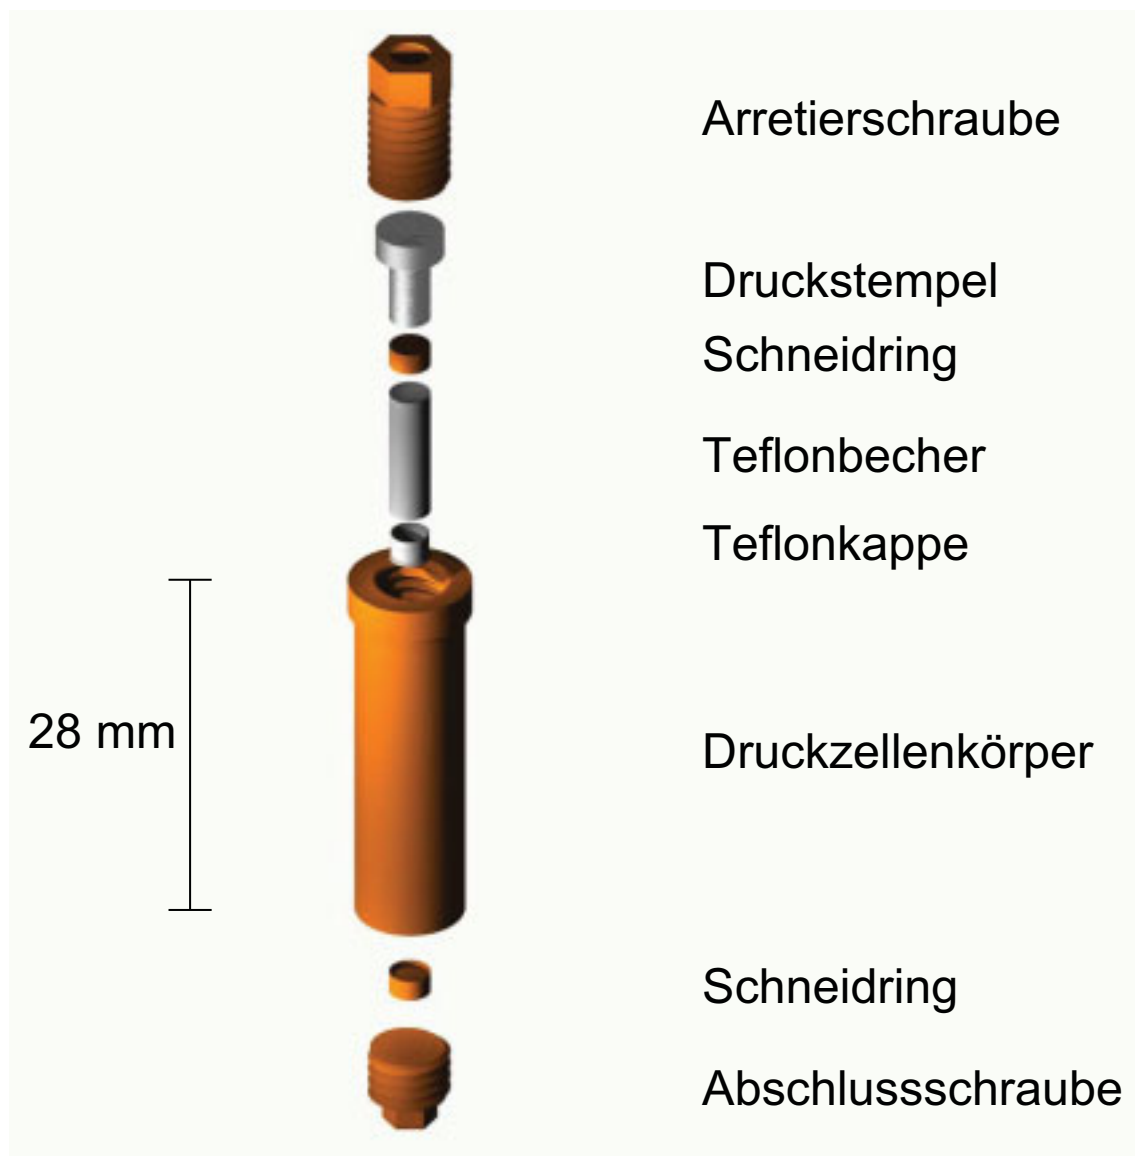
Schemazeichnung der für die Messungen an UGe_2 verwendeten Druckzelle.
